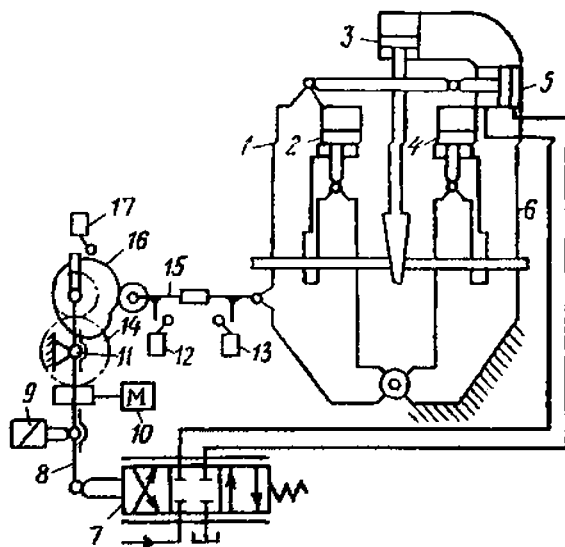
Схема системы оплавления и осадки стыкосварочной машины
